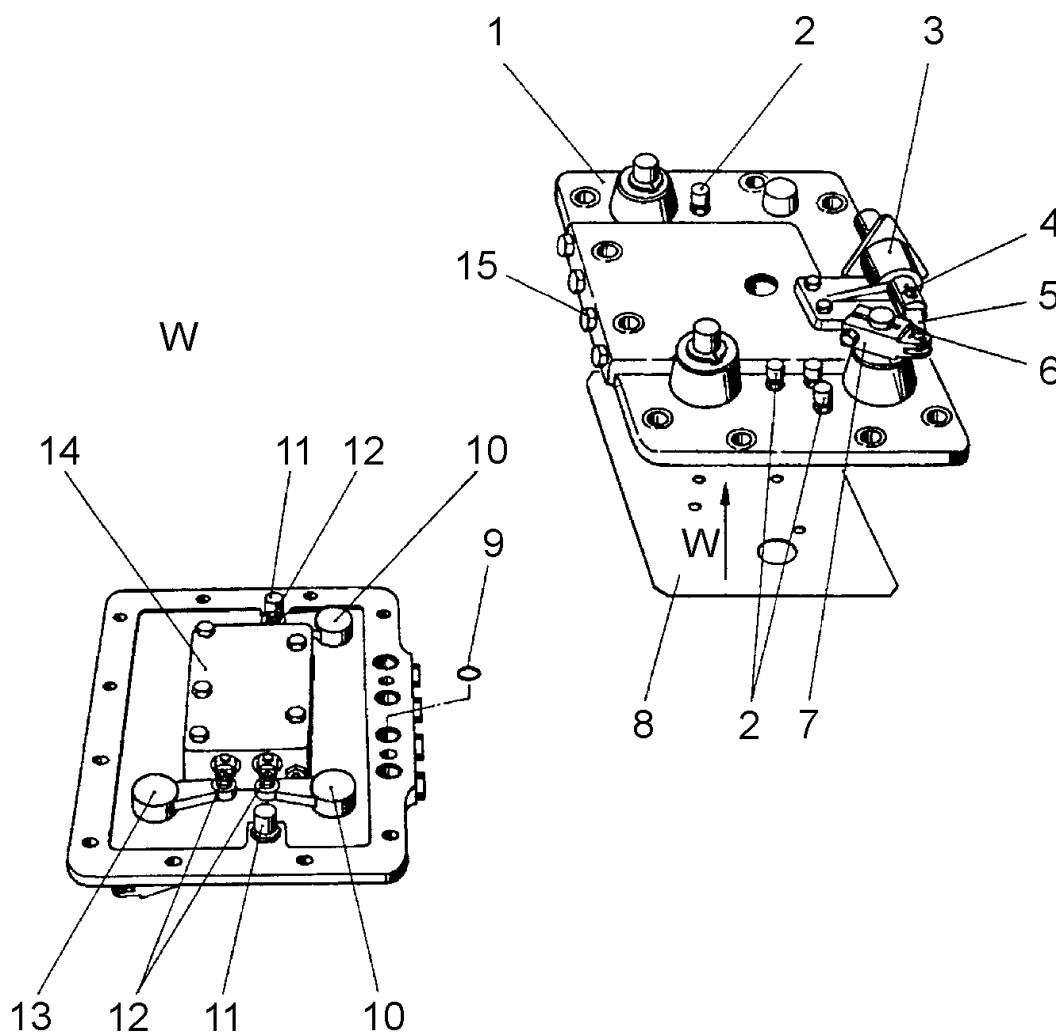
С.13. Крышка управления коробкой передач (вид сверху и снизу)
